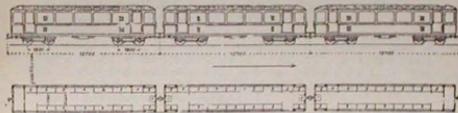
Ferrovia elevata e sotterranea di Berlino vista e pianta delle vetture.
